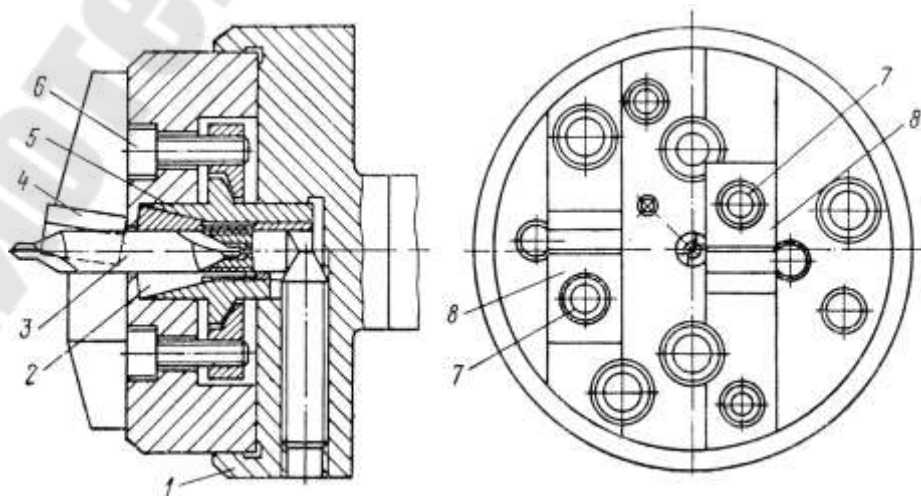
Эскиз патрона для подрезки и одновременной зацентровки торцов заготовок
